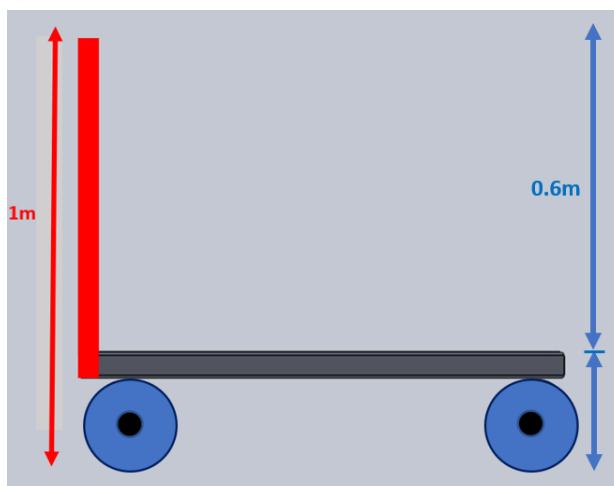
Ilustración de las dimensiones de la estructura de empuje [fuente propia]
